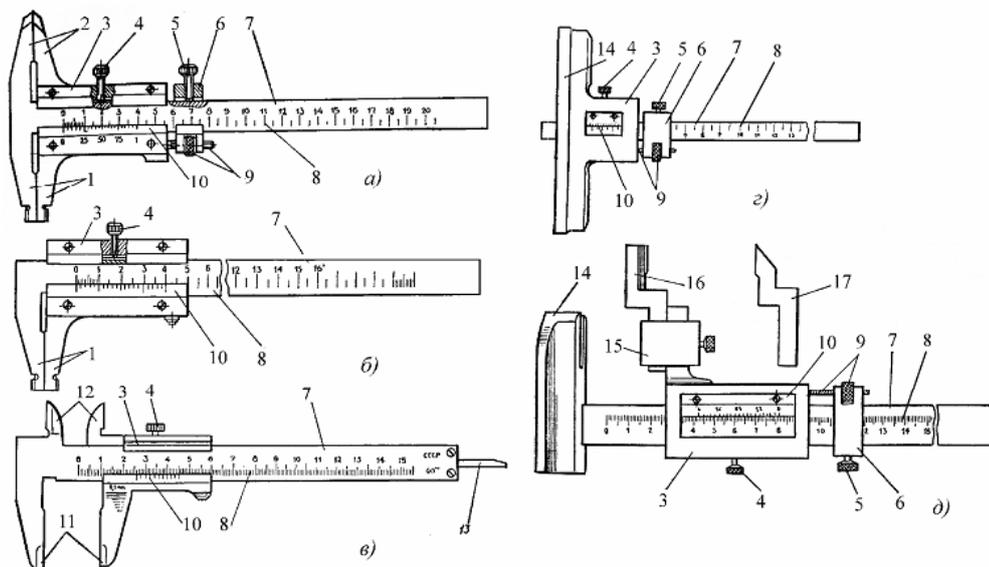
Штангенциркули (а – в), штангенглубиномер (з) и штангенрейсмас (д):
